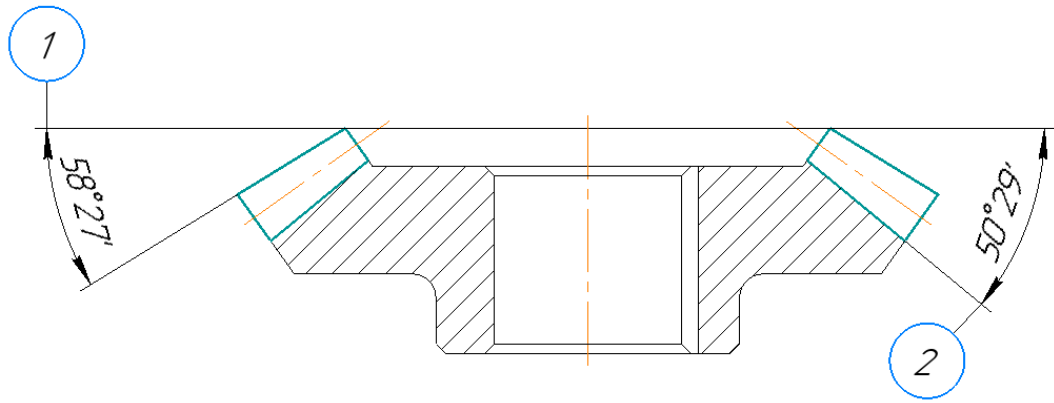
Ескіз обробки заготовки на операції 025
